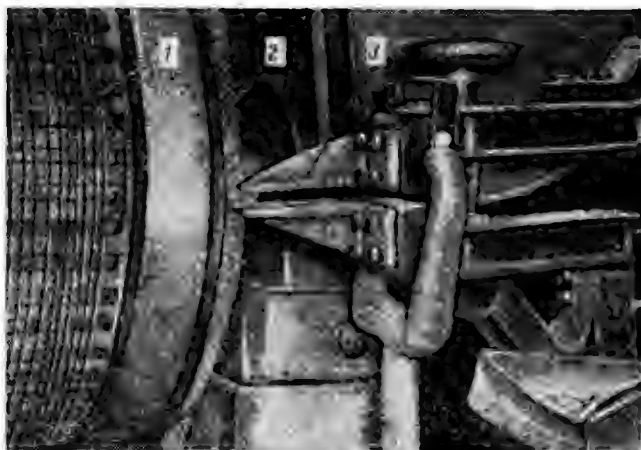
Сварочный агрегат для пайки соединительных скобочек разрезных обмоек якорей тяговых двигателей:
